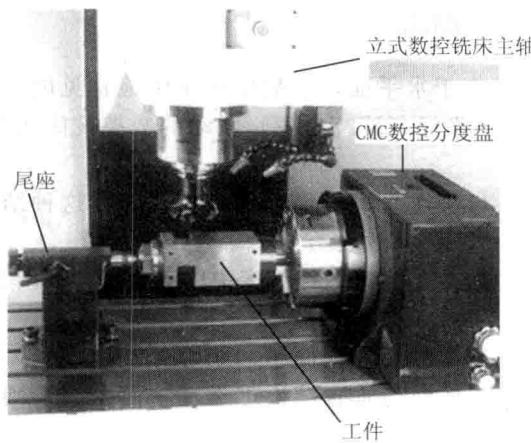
立式数控铣床配数控转盘实现四轴联动加工
